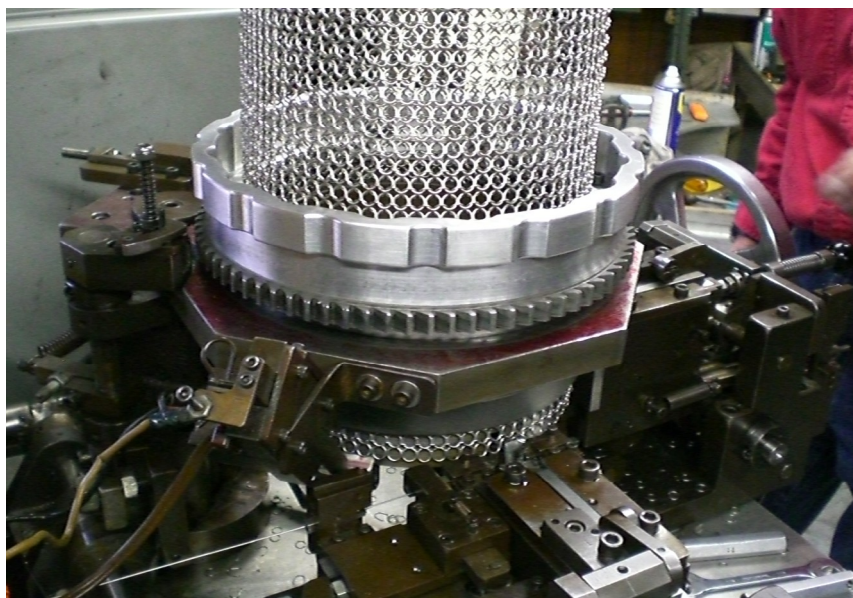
Rundflechtmaschine mit Spiralsteuerung,
